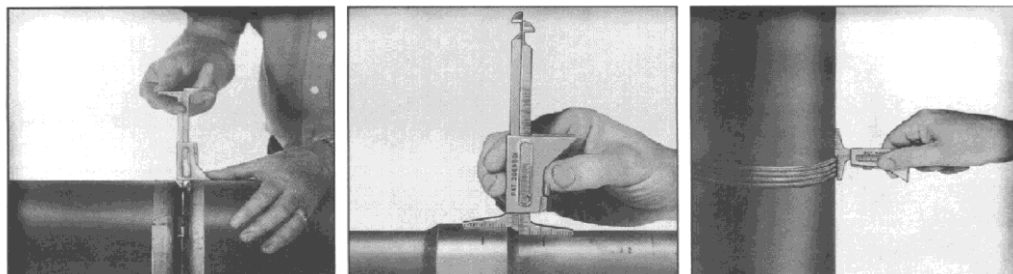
Inspección visual y medición de juntas soldadas.
